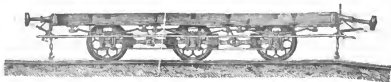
Prospetto d'un treno di vettura di 2.ª classe.
